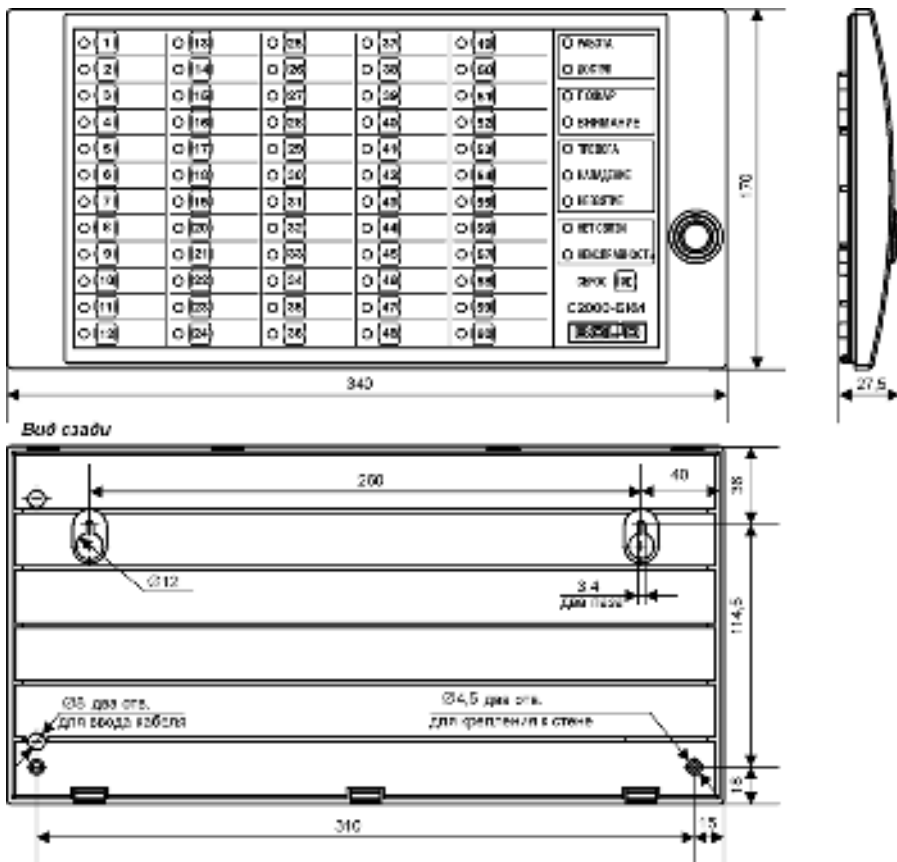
Внешний вид, габаритные и установочные размеры блока
